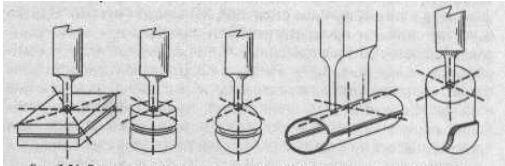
Расположение волновода при сварке деталей несложной формы
